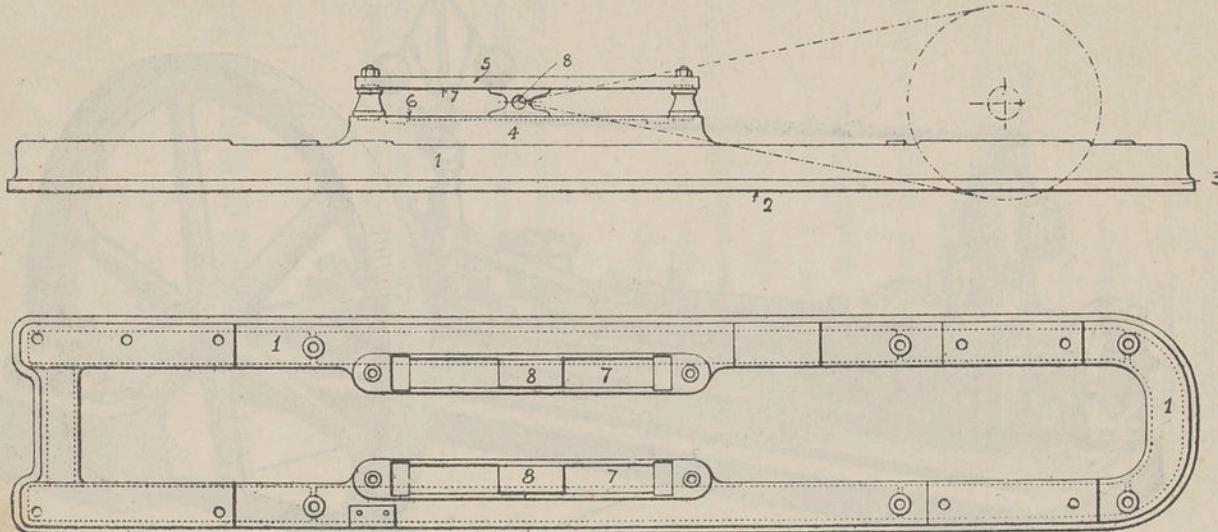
SUPPORTE PARA UMA MACHINA HORIZONTAL
